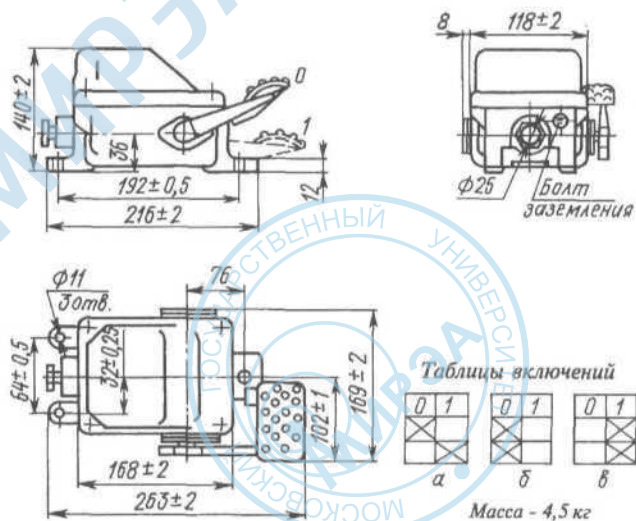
Габаритные, установочные размеры и масса выключателя типа НВ-741
